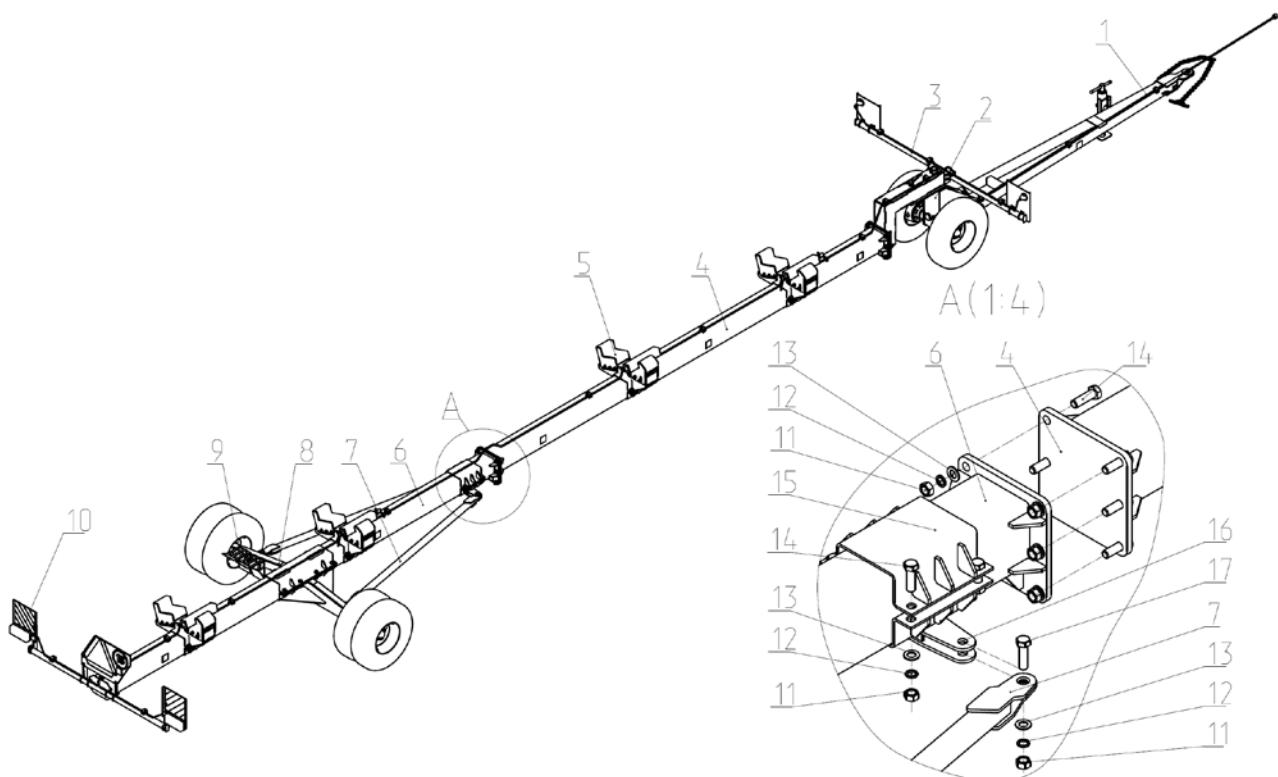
ЖНПС 11.000 Приспособление для перемещения адаптера.
